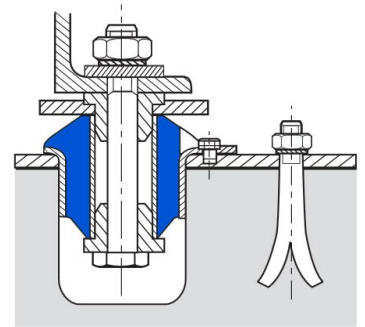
Montaje entre pie de la maquina y chasis metálico.
